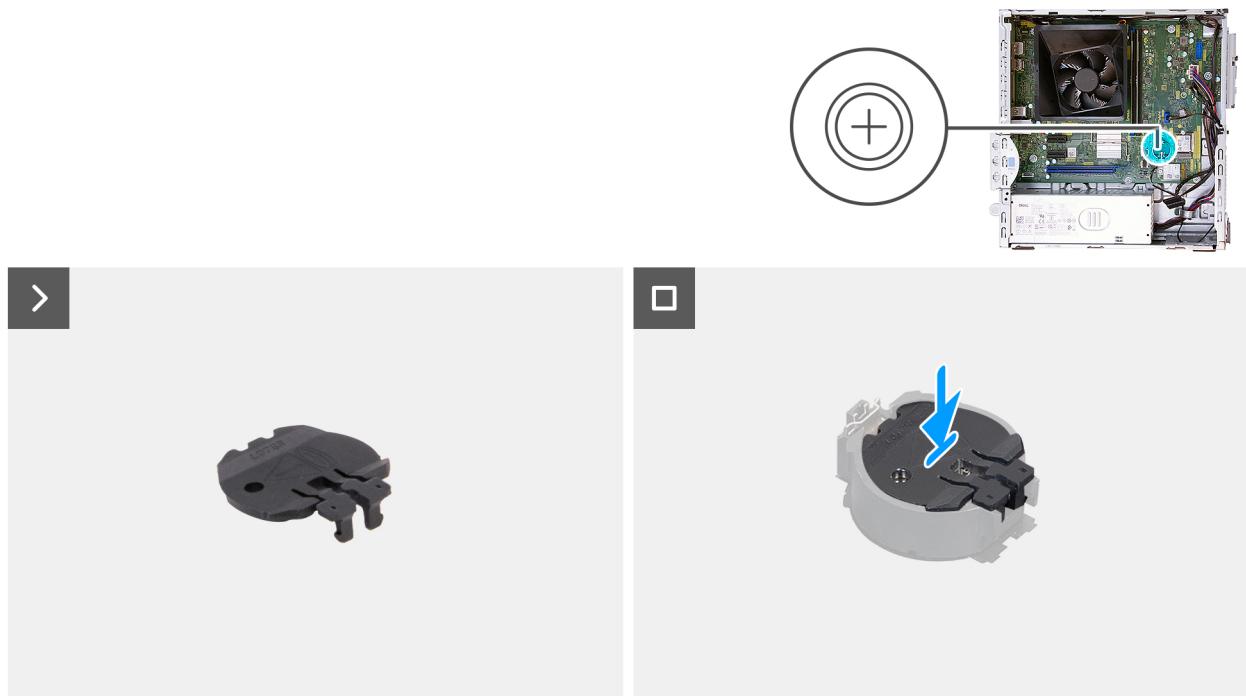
Instalación de la cubierta de la batería de tipo botón
